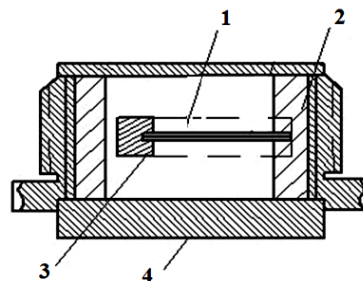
Конструкція ПГ АГС: 1 – ПЕ; 2 – стрижень; 3 – ІМ; 4 – герметичний корпус
